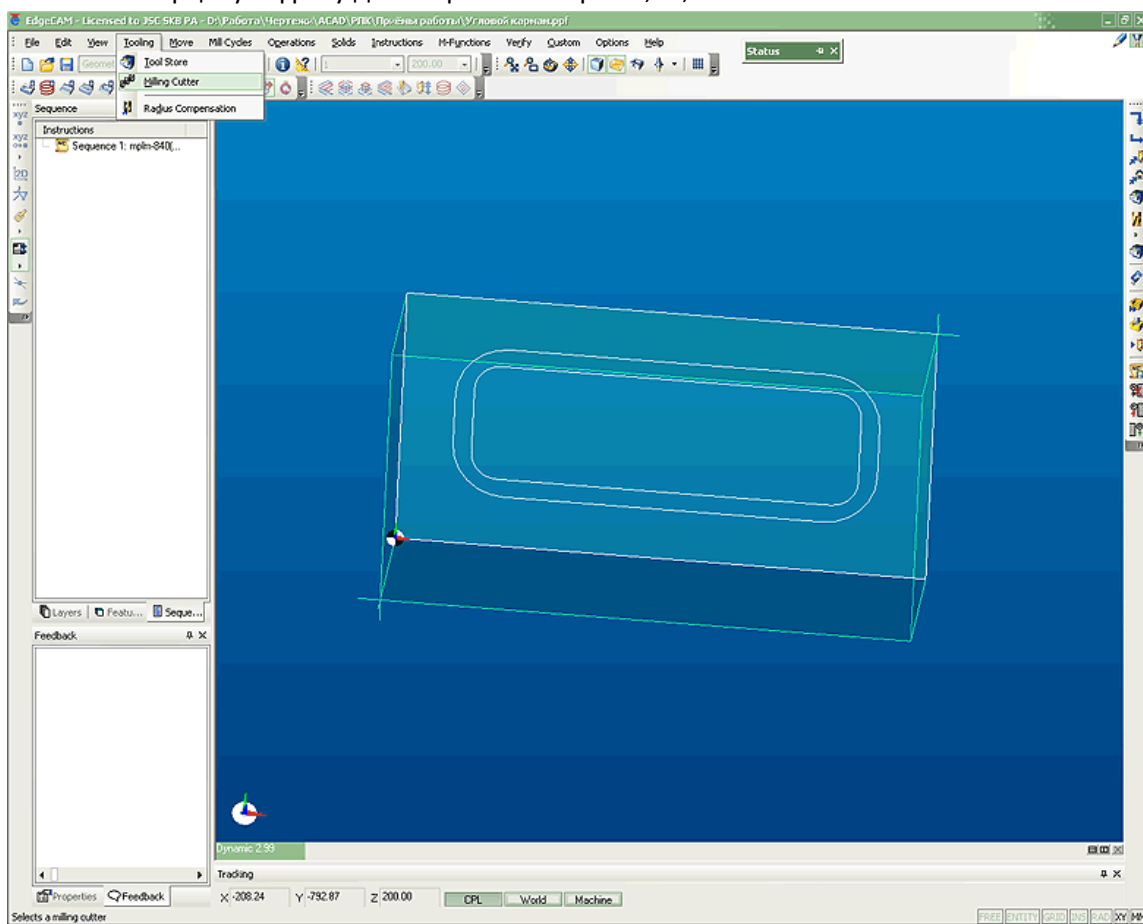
Edgecam. Назначаем торцевую фрезу диаметром 10мм
